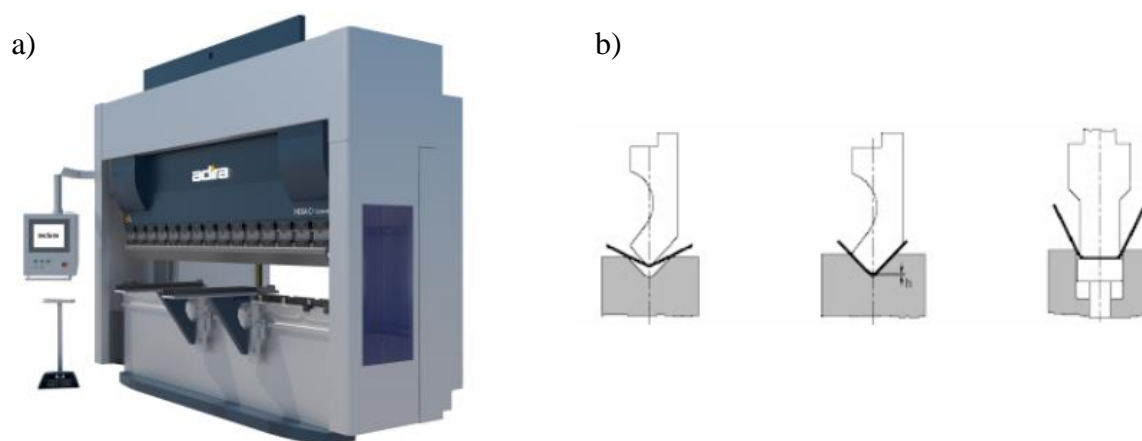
a) Quinadora de moldagem de AEF (ferrol2industria@) e b) Processo de quinagem (Arsedys@)
